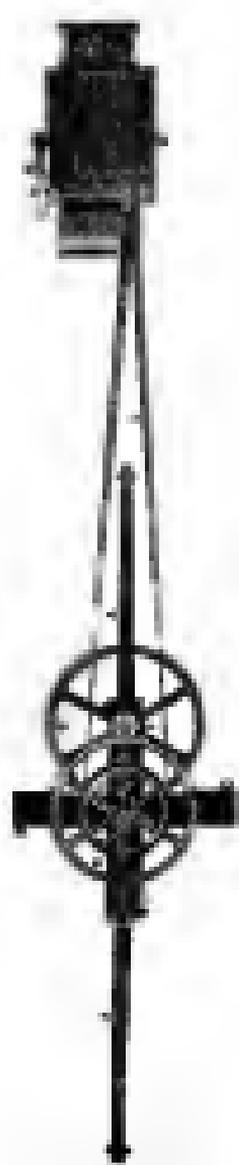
Machine à vapeur et moulin de M. Flett (plan).
